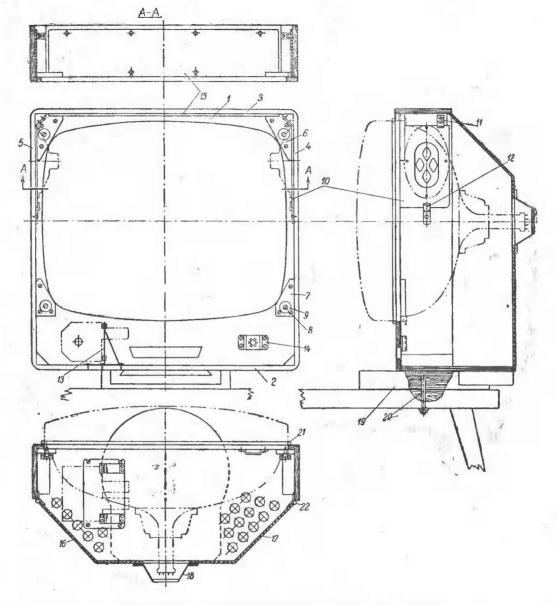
Общий вид ящика телевизора и поворотного устройства.
